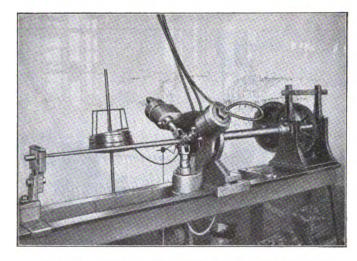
Wickelmaschine mit kegeliger Spindel und Druckluft-Wickelrollen.
